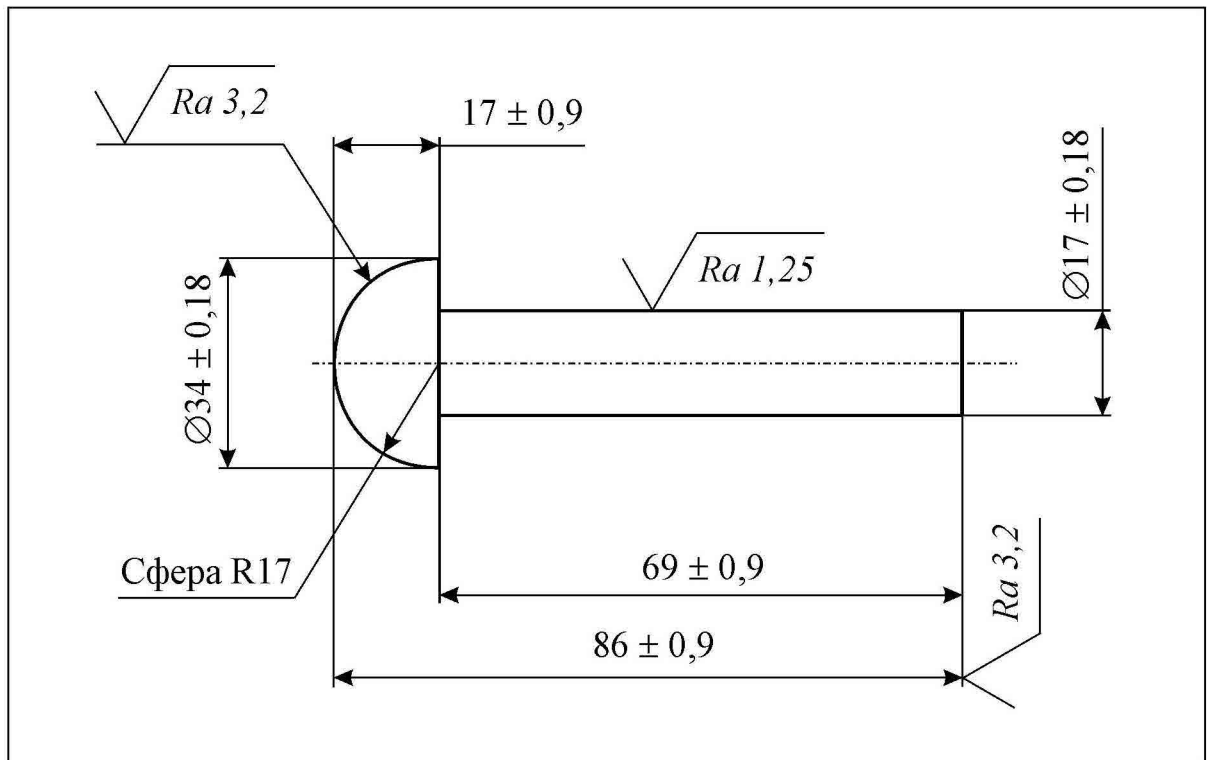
Ескіз деталі після висаджування сферичної головки
